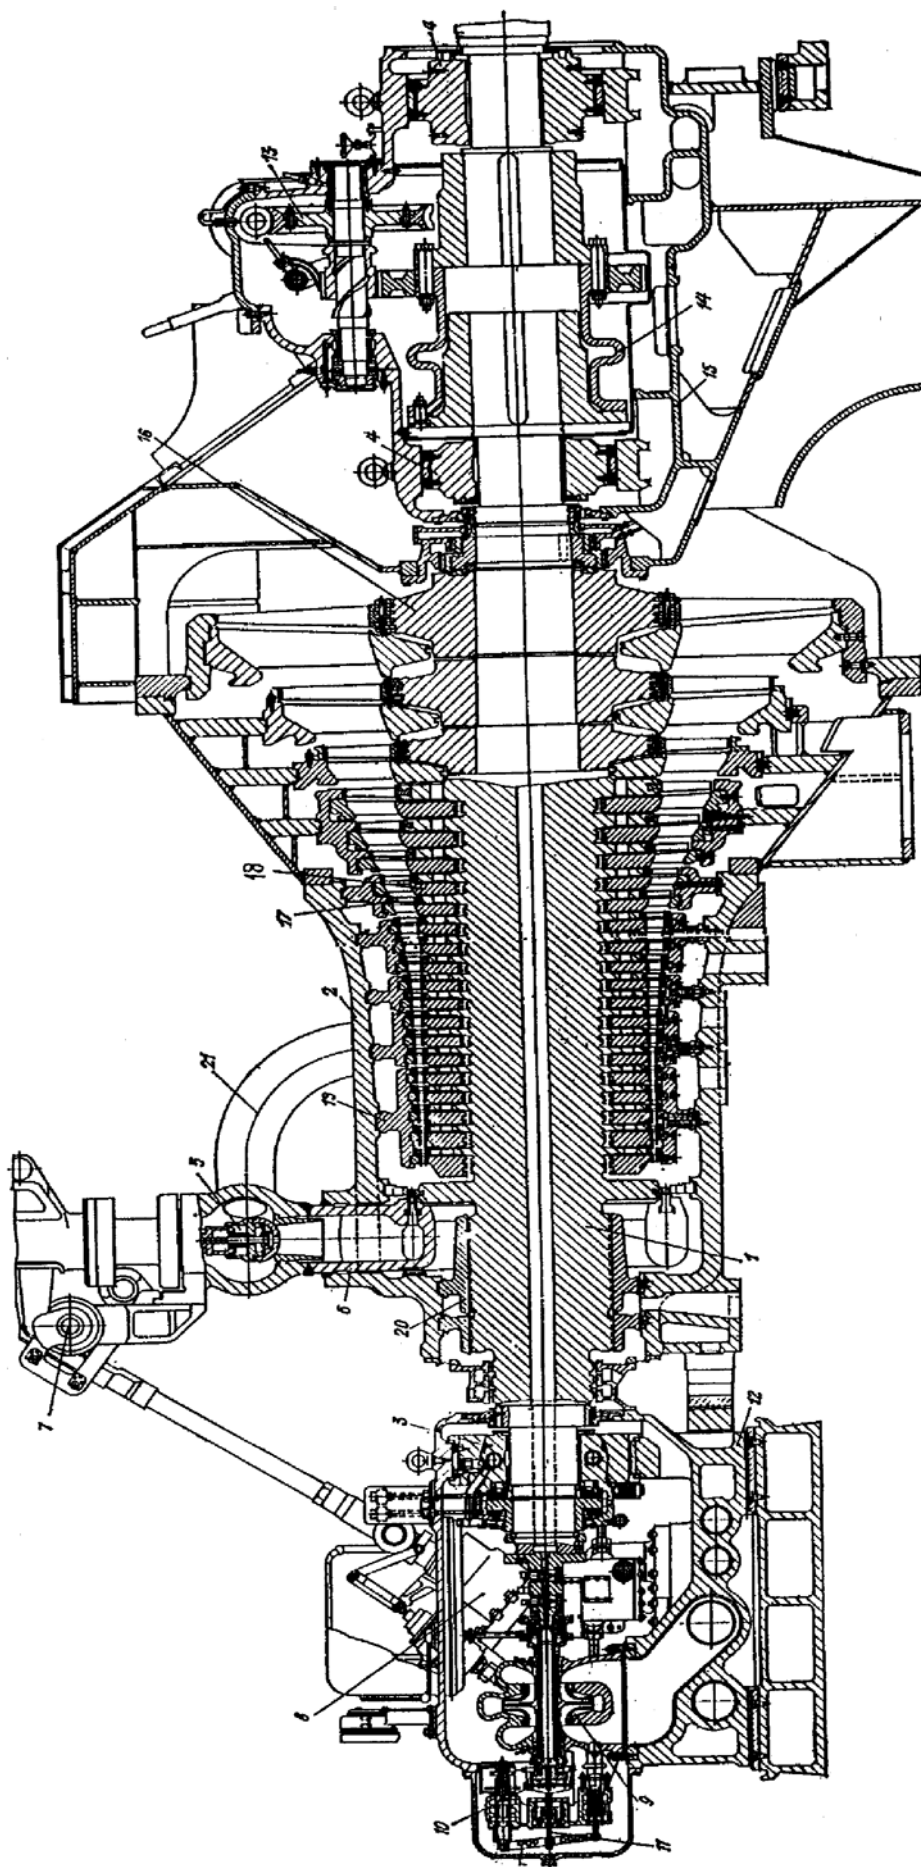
Продольный разрез турбины К-50-90: 1 – ротор турбины; 2 – корпус турбины; 3 – опорно-упорный подшипник; 4 – опорный подшипник; 5 – регулирующий лопатки; 6 – сопловая коробка; 7 – кулачковый вал; 8 – сервомотор; 9 – главный масляный насос; 10 – регулятор скорости; 11 – следящий золотник; 12 – картер переднего подшипника; 13 – валоповоротное устройство; 14 – соединительная муфта; 15 – выхлопной патрубков турбины; 16 – насадные диски; 17 – рабочие лопатки; 18 – диафрагмы; 19 – обоймы диафрагм; 20 – обоймы диафрагмы; 21 – перепускная труба (от стопорного к регулирующему клапану).
